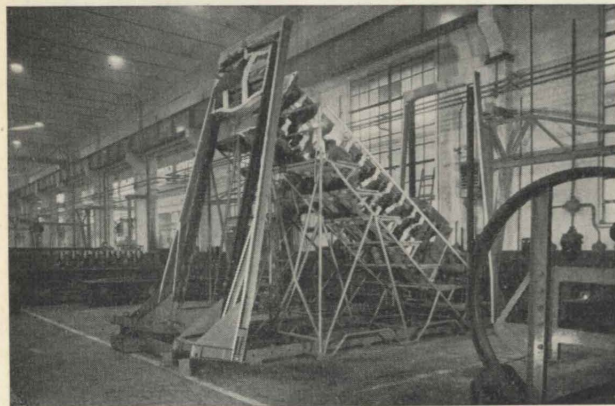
Posizionatore per saldatura incastellatura motore 2312 SF.
